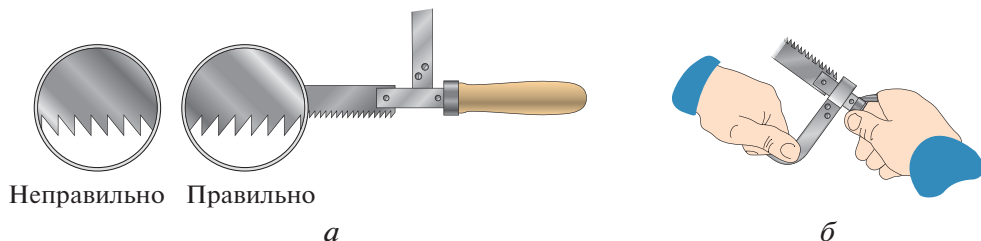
Подготовка ножовки к работе: а — установка полотна в ножовку; б — натяжение ножовочного полотна
